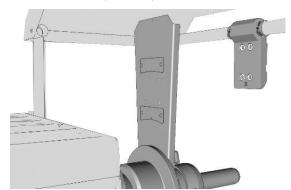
Положение калибровочной пластины для калибровки УЗД
